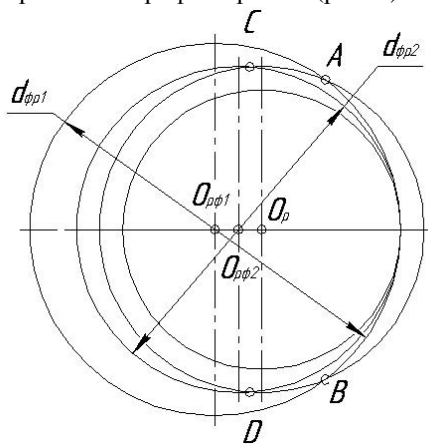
Схема порівняння величини дуги контакту нарізаємої різьби з інструментами різного діаметра
